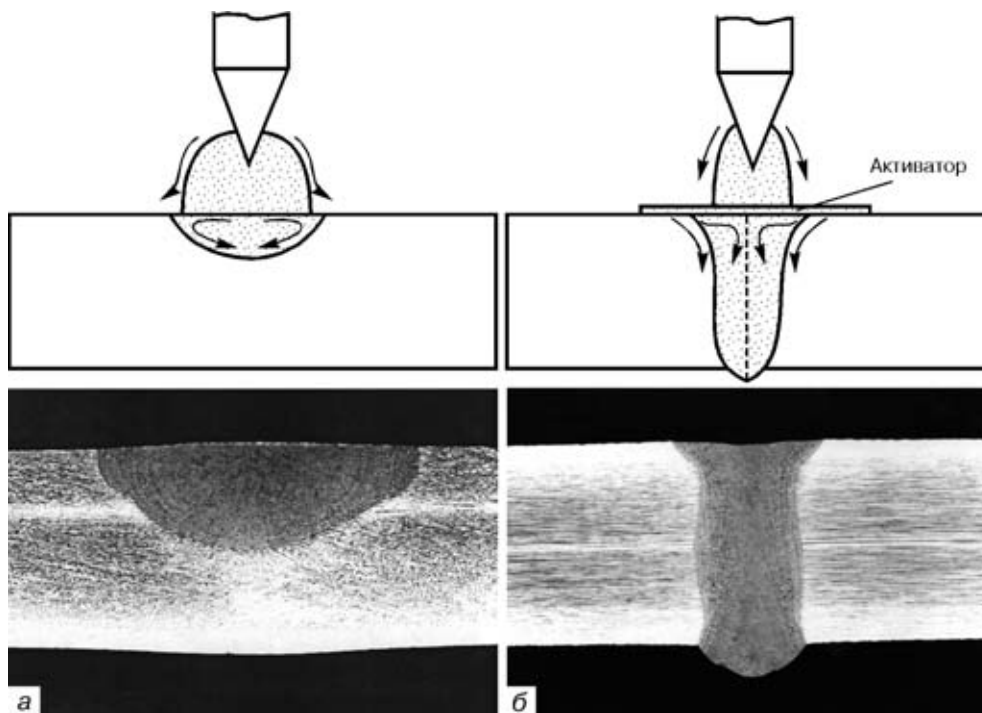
Принципиальная схема процессов дуговой сварки и макрошлифы сварного соединения стали 304L толщиной 6 мм, выполненные способами сварки ТИГ (а) и А-ТИГ (б)
